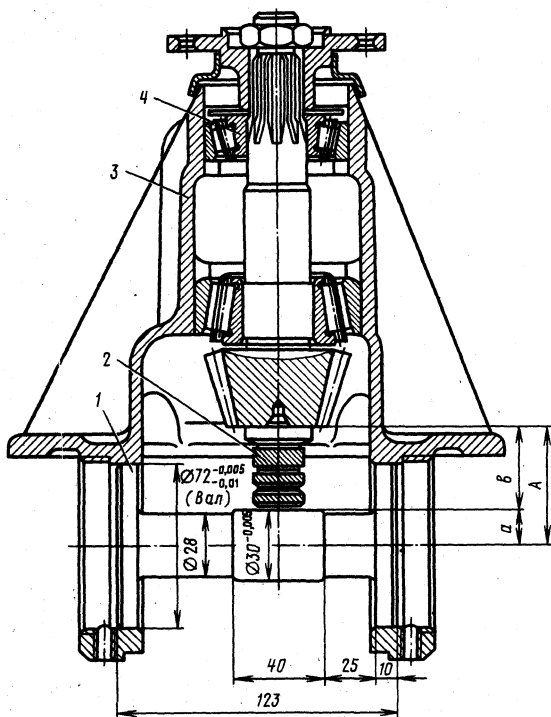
Определение сборочного размера A редуктора автомобиля «Москвич»:
